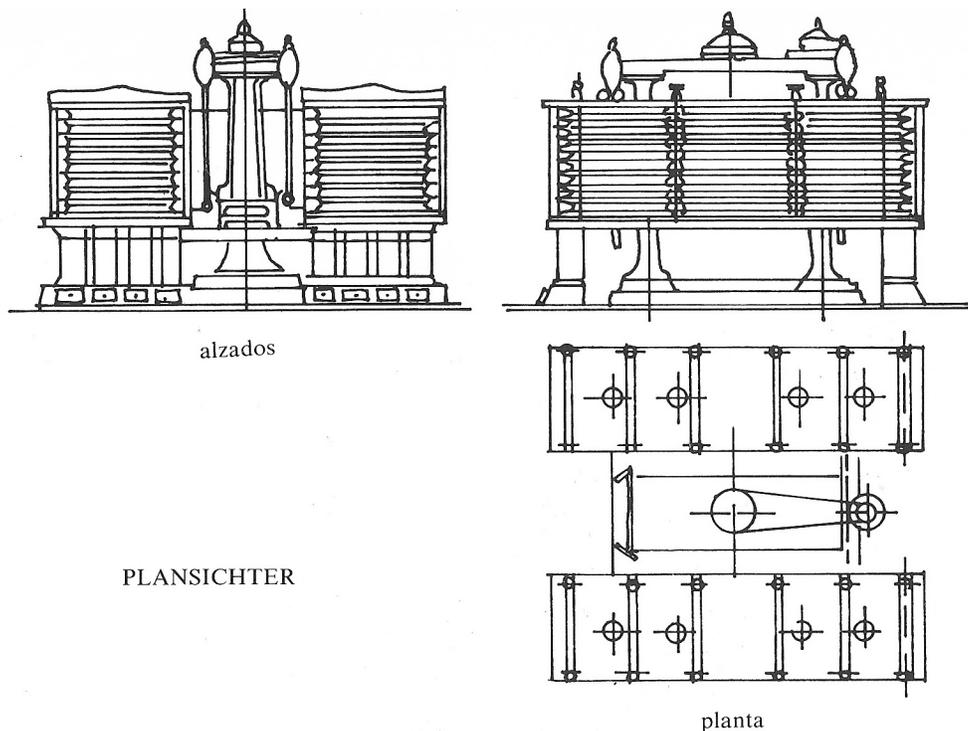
Planos de alzados y planta de un plansichter. (CARRERA DE LA RED, Miguel Ángel: *Las fábricas de harina en la provincia de Valladolid*, Caja de Ahorros Provincial de Valladolid, 1990).
